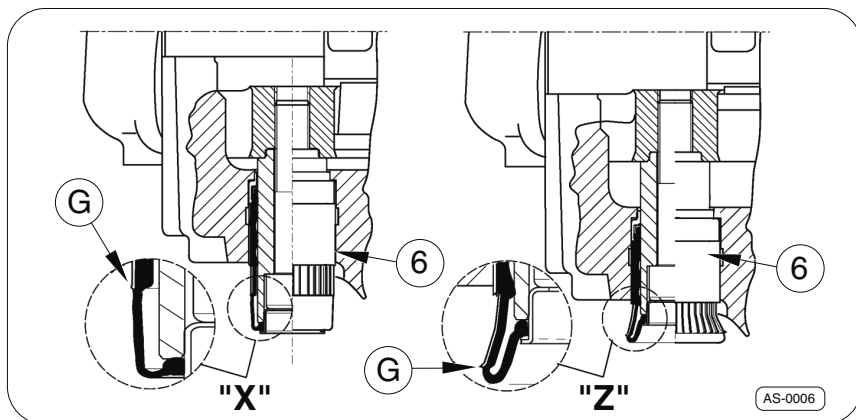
· Дисковый тормозной механизм KNORR типа SN6
